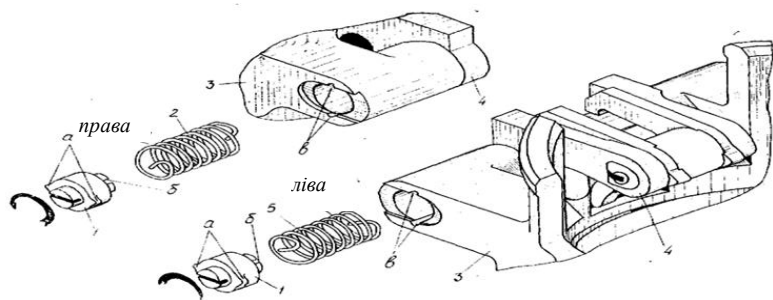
Встановлення пружин лопаток запобіжника:
